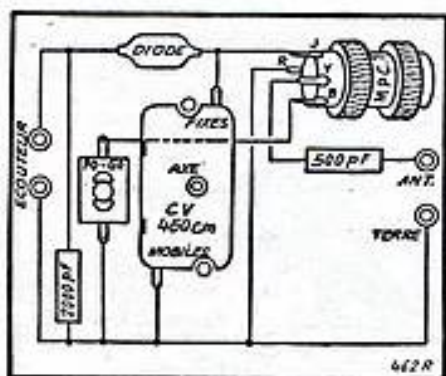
Le montage sur plaquette isolante, vue arrière.
